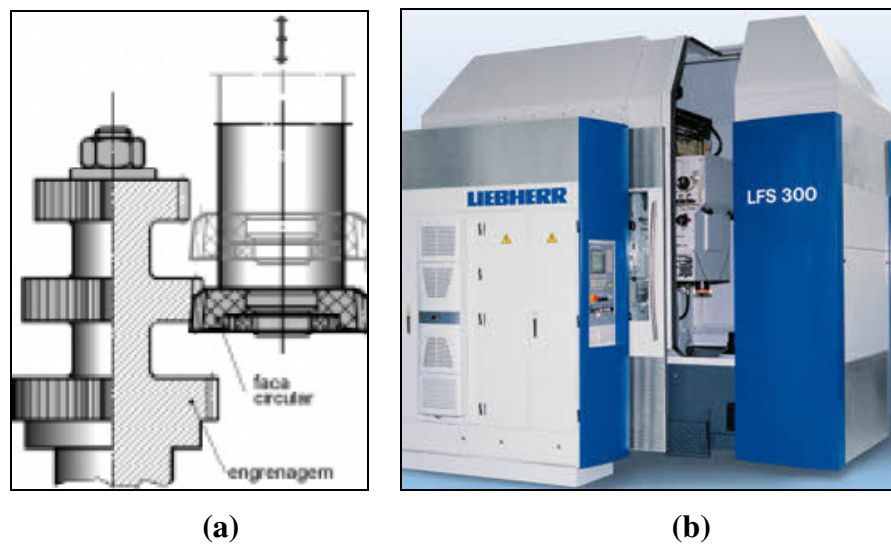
Máquina para geração por dentes Reto. a) Interno – b) Externo
